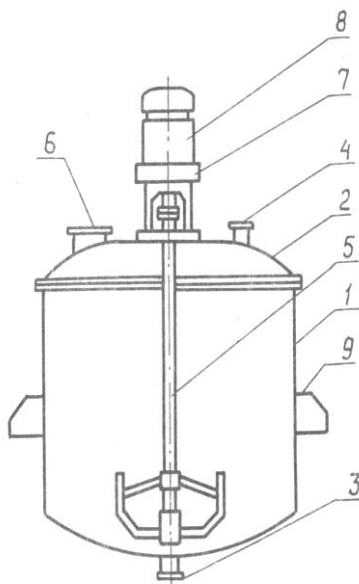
Schema echipamentului pentru amestec: 1-corp; 2-capac sferic; 3,4-racord; 5-agitator; 6-gura; 7-reductor mecanic; 8-motor electric; 9-suport.
